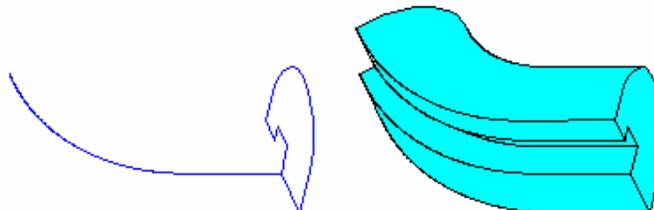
Эскизы и элемент, образованный кинематической операцией
